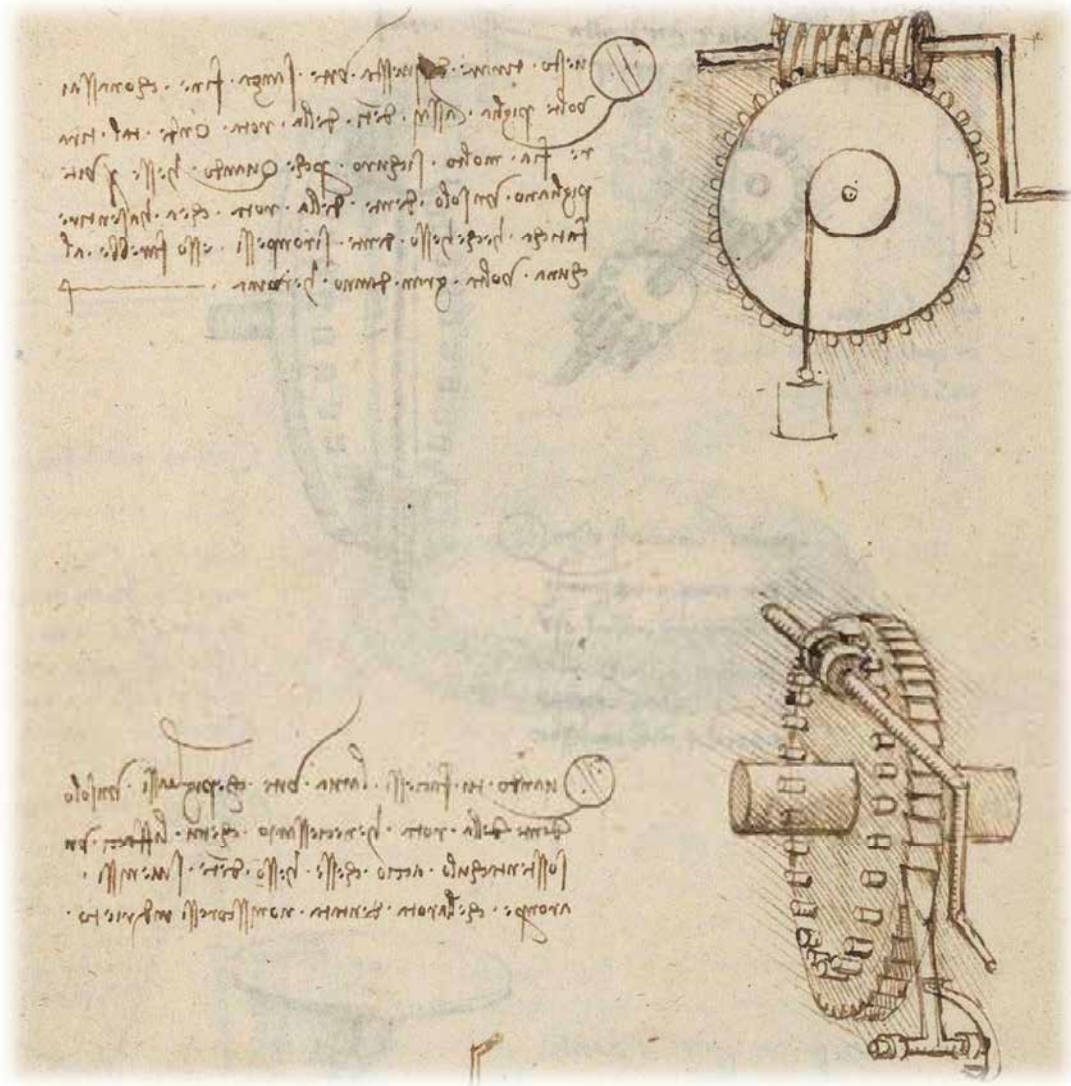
Tornillo sinfín que engrana con una rueda dentada (engranaje helicoidal).
